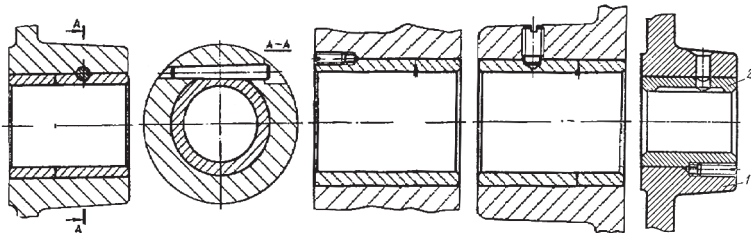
Варианты крепления втулок подшипников скольжения
